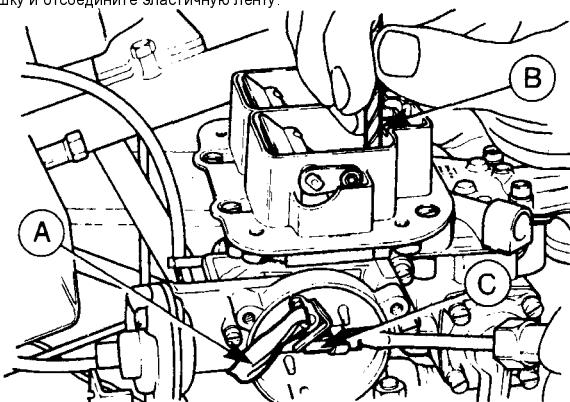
Проверка хода заслонки под воздействием разряжения - карбюратор WEBER. А - Эластичная резиновая лента. В - Сверло (щуп для измерения зазоров). С - Тяга.
